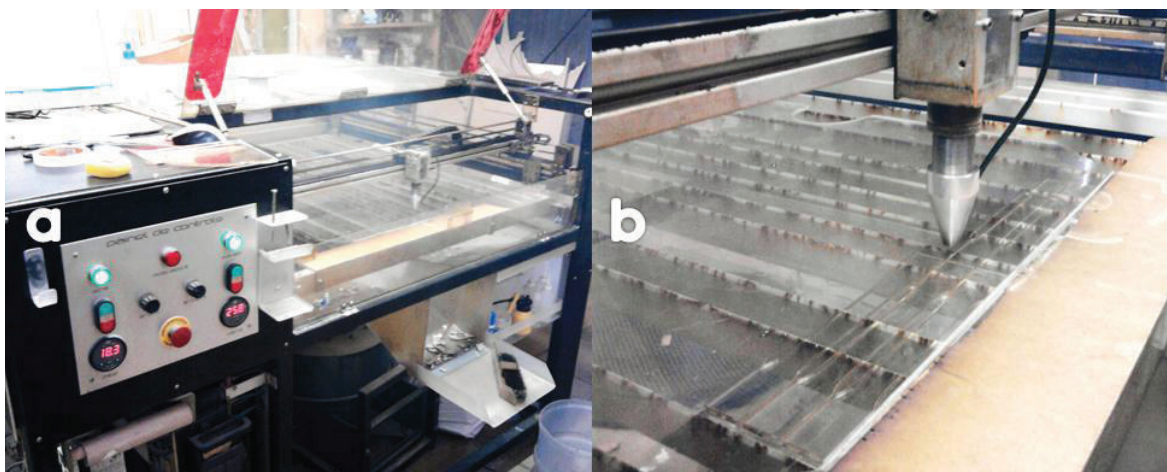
a) Mesa de corte a laser utilizada; b) Execução do corte dos corpos de prova RN+NPG.
